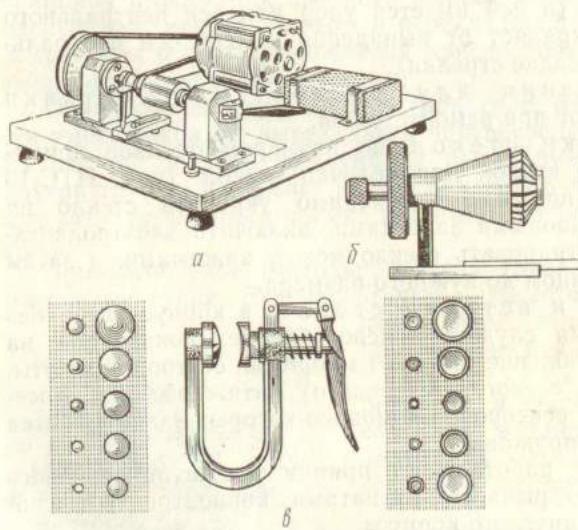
Станок и приспособления для обточки и вставки стекол:
